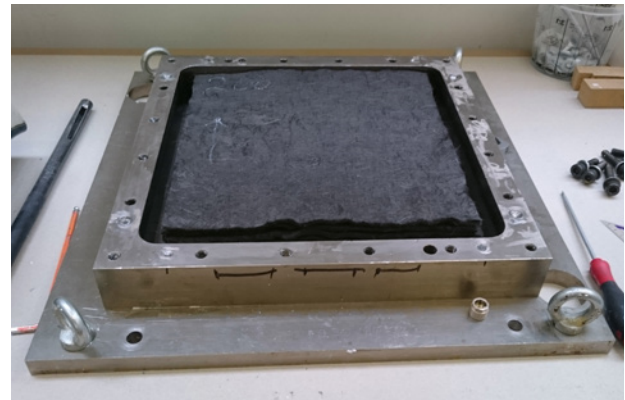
Plattenwerkzeug bestückt mit rCF-Vliesstoffen. Quelle: Schmuhl
